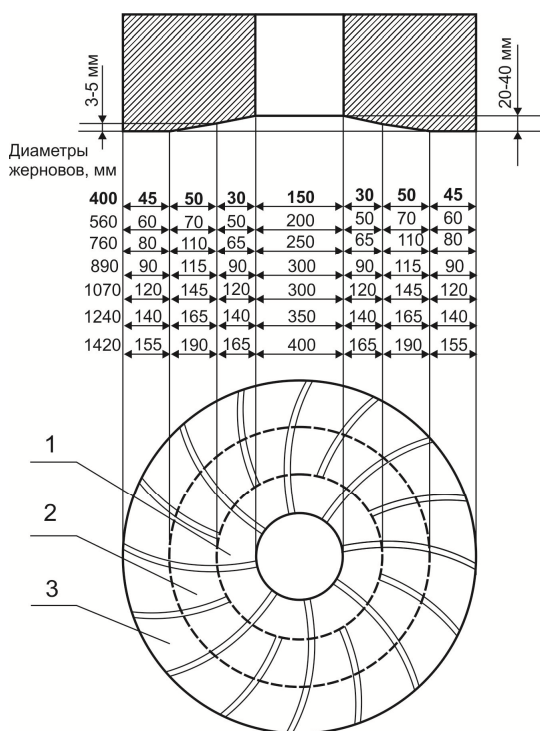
Разбивка рабочей поверхности жернова
